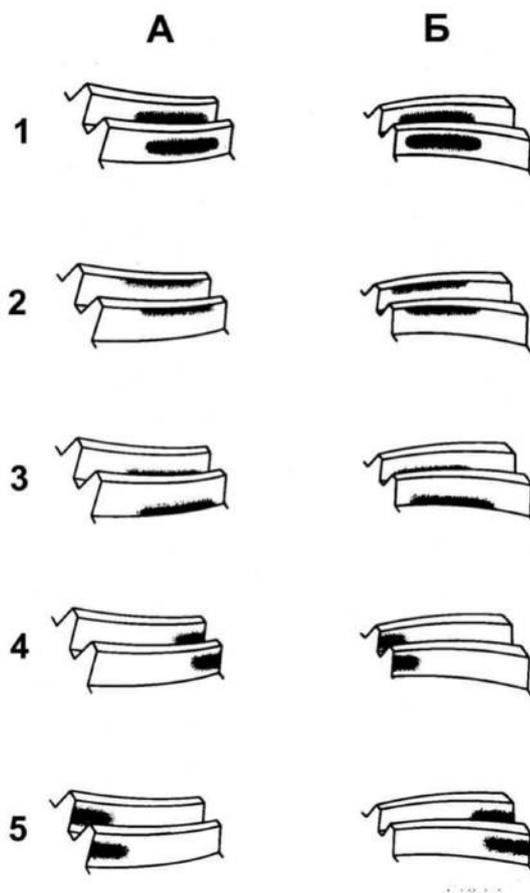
Пятно контакта в шестернях главной передачи: А - стороны переднего хода; Б - стороны заднего хода; 1 - правильное расположение пятна контакта; 2 - пятно контакта расположено на вершине зуба - для исправления подвинуть ведущую шестерню к ведомой; 3 - пятно контакта расположено у основания зуба - для исправления отодвинуть ведущую шестерню от ведомой; 4 - пятно контакта расположено на узком конце зуба - для исправления отодвинуть ведомую шестерню от ведущей; 5 - пятно контакта находится на широком конце зуба - для исправления подвинуть ведомую шестерню к ведущей
